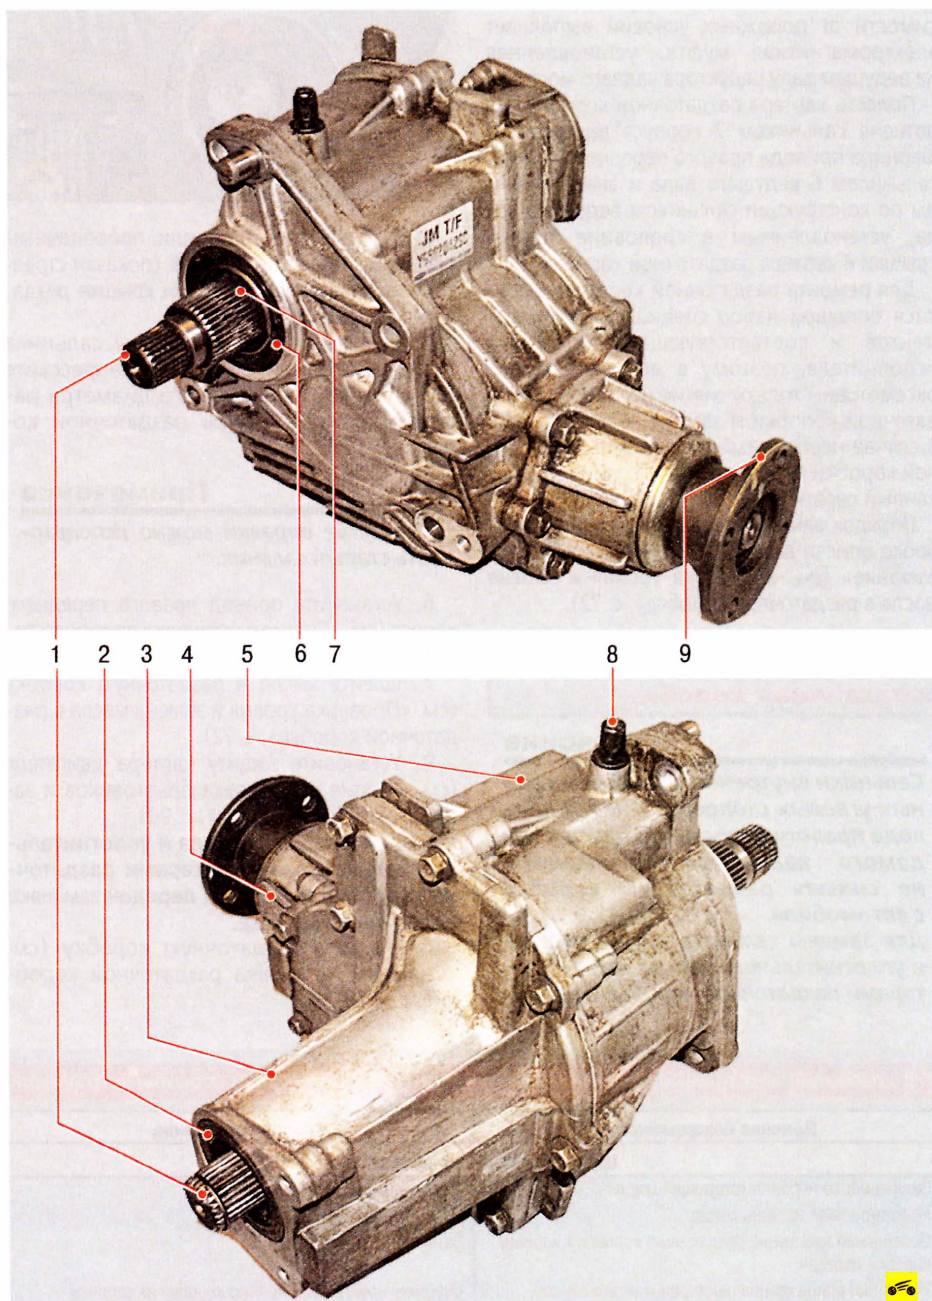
Раздаточная коробка: 1 — промежуточный вал; 2 — сальник корпуса внутреннего шарнира привода правого переднего колеса; 3 — боковая крышка картера раздаточной коробки; 4 — задняя крышка картера раздаточной коробки; 5 — картер раздаточной коробки; 6 — сальник ведущего вала; 7 — ведущий вал; 8 — сапун; 9 — фланец ведомого вала
